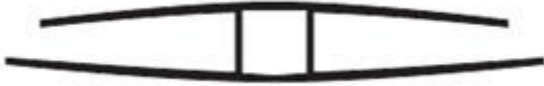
а. Типичный (неразъемный) поликарбонатный соединительный профиль (повернутая «Н»)
